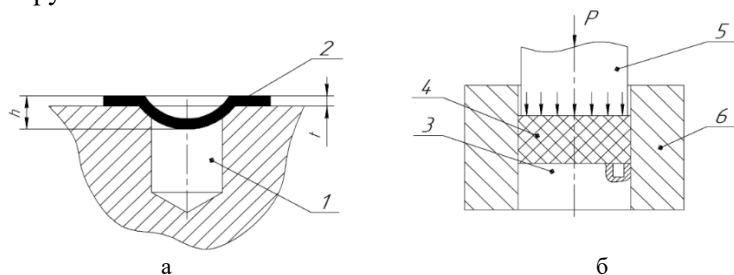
Схема измерений контактных напряжений с помощью фольговых датчиков:
